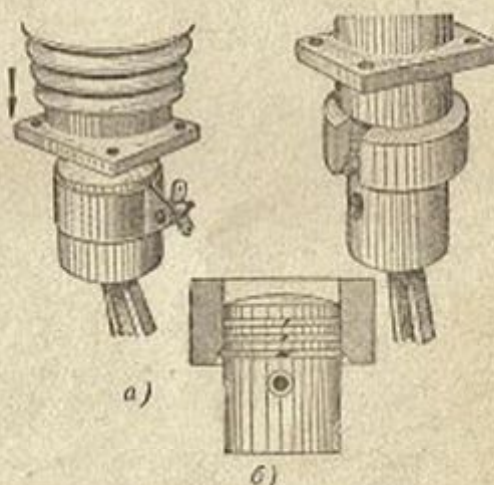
Приспособление для сжатия поршневых колец при надевании на поршень
